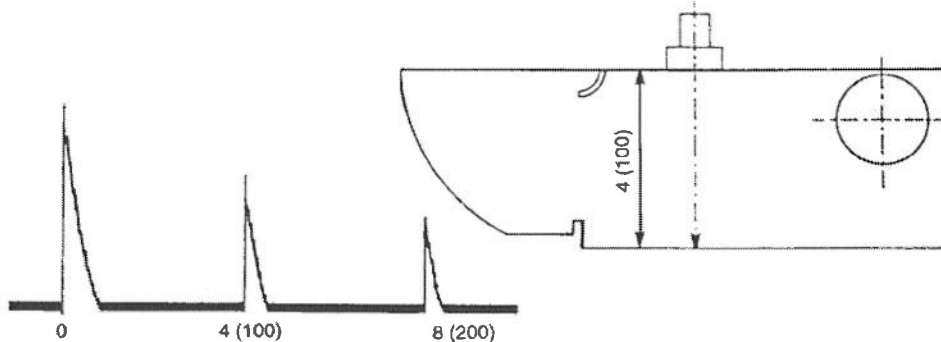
แท่งปรับมาตรฐานของ International Institute of Welding (IIW)
